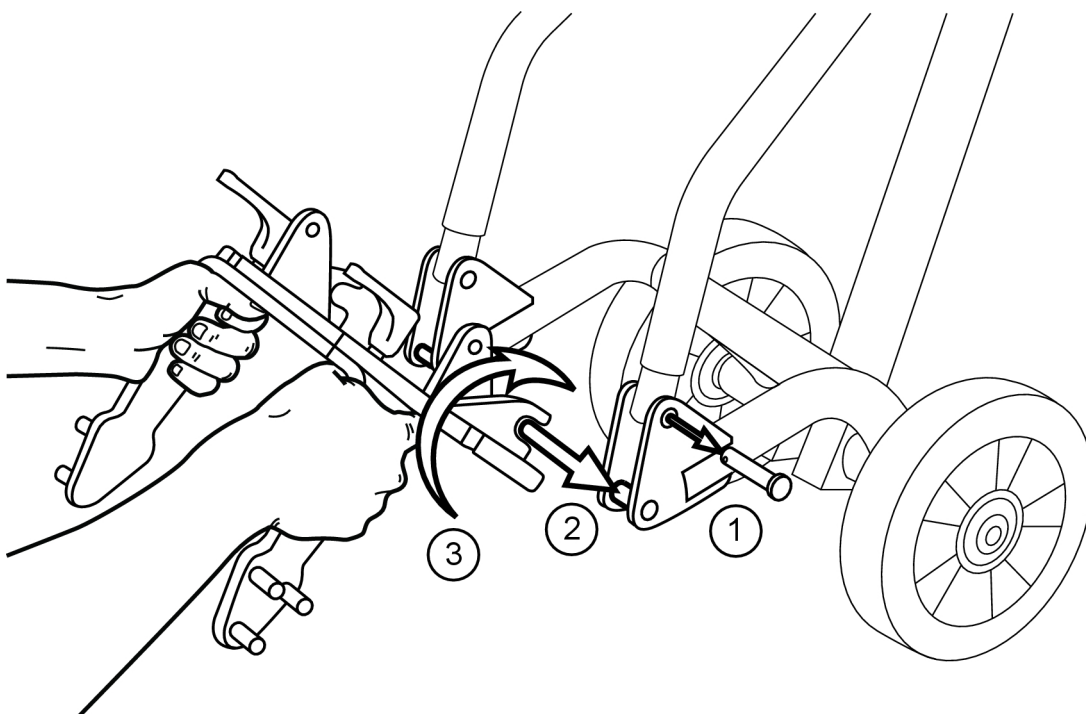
Установка переходника для шлифовки кромок, операции 1—3.
